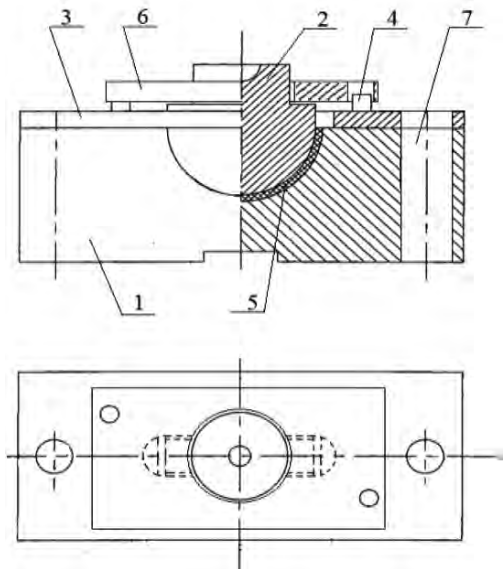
Схема приспособления для замера деформации в подшипниковом гнезде
